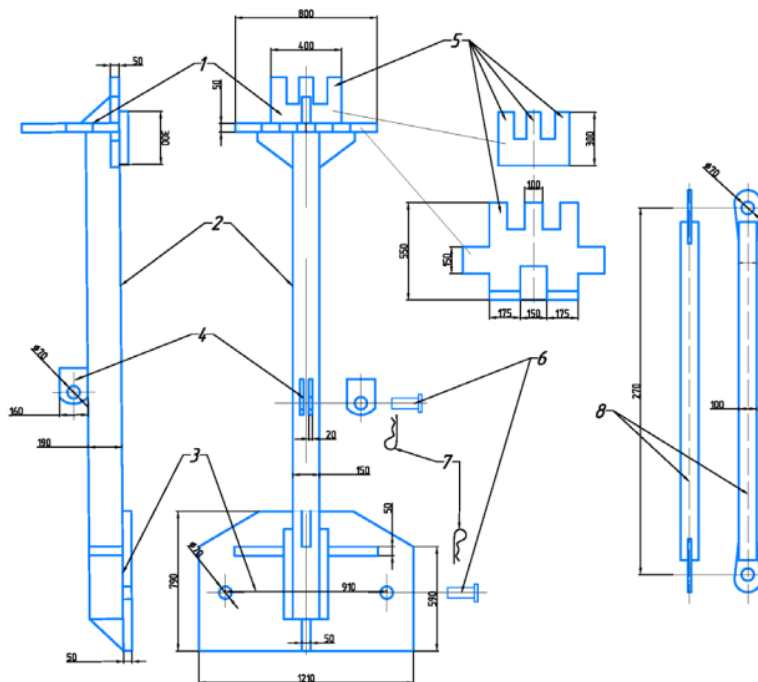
Конструкция ОКН: 1 – рабочий орган; 2 - стрела; 3 – опорная плита; 4 – проушина для крепления распорной штанги; 5 – перья рабочего органа; 6 – крепежные пальцы; 7 – фиксирующие шплинты; 8 – распорная штанга
